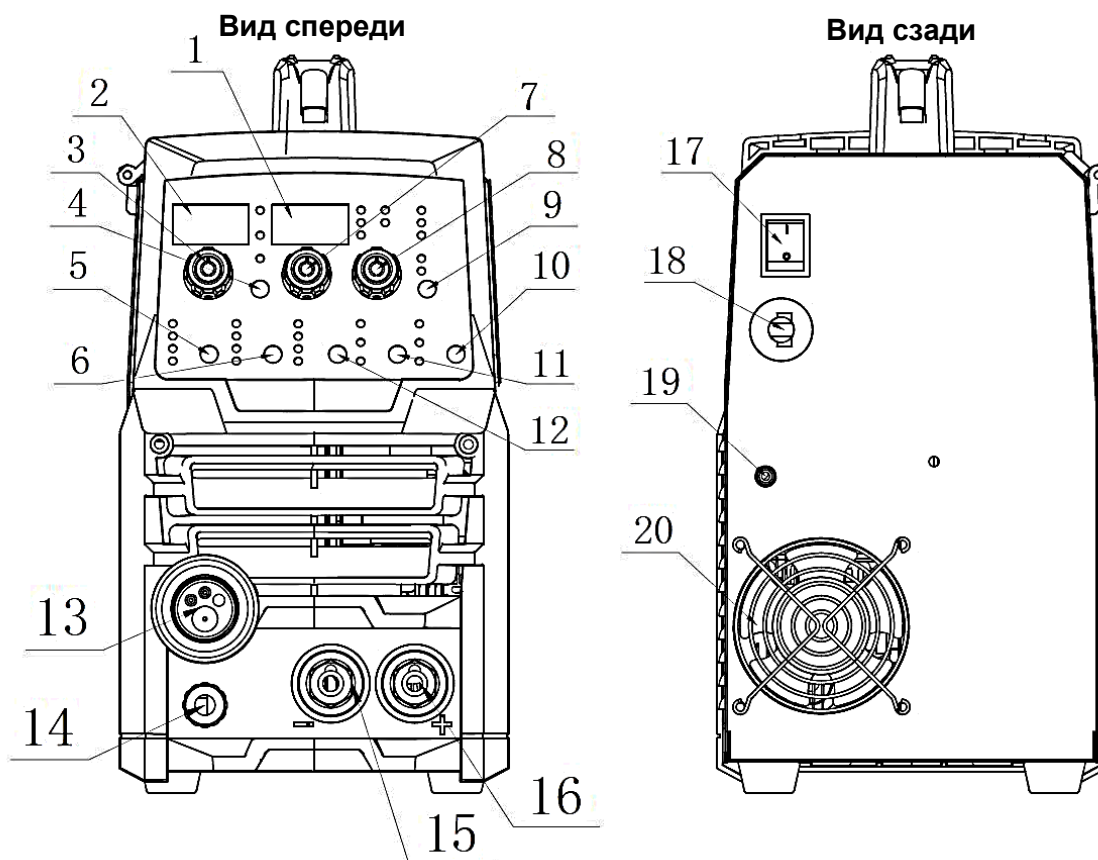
Общий вид (Инверторный сварочный полуавтомат)
